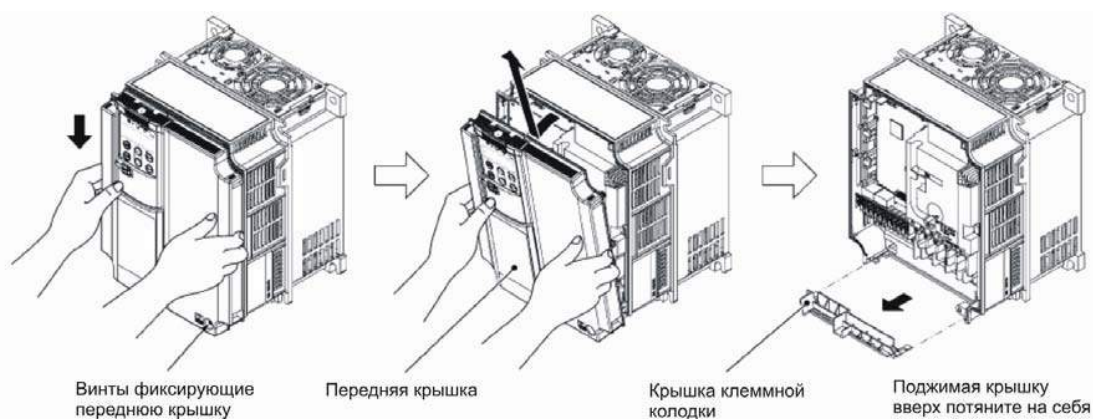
Установка и снятие передней крышки и крышки клеммной колодки (FRN11G1■-4□)
